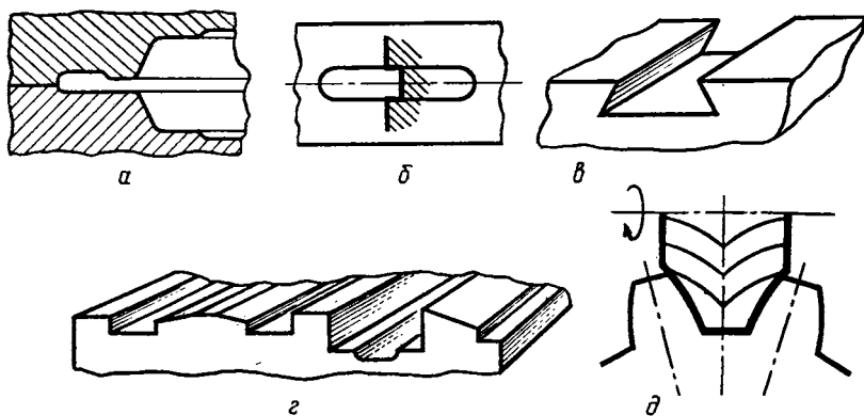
Поверхности, обрабатываемые фрезерованием:
